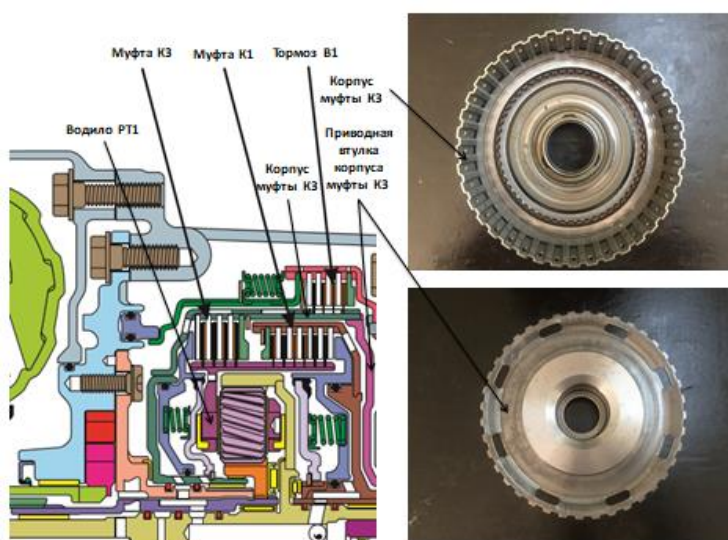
Устройство и назначение корпуса муфты К3 и его приводной втулки
